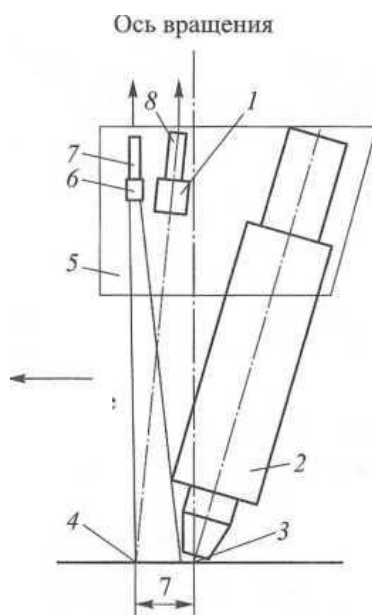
Лазерный датчик слежения за стыком: 1 — фильтр и система линз; 2 — сварочная головка; 3 — сварочная ванна; 4 — полоска света; 5 — корпус; 6 — система линз; 7 — световод; 8 — волоконный световод
